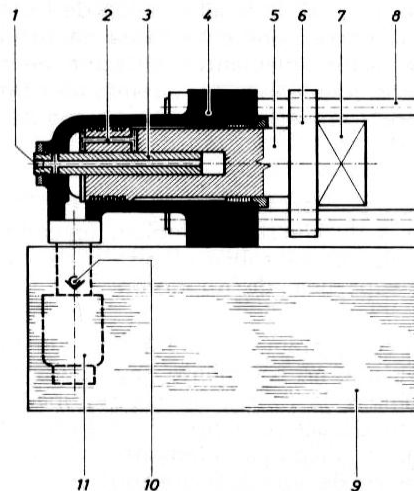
Sección longitudinal de un grupo de cierre de moldes con doble rodillera, accionado por cilindro hidráulico.
